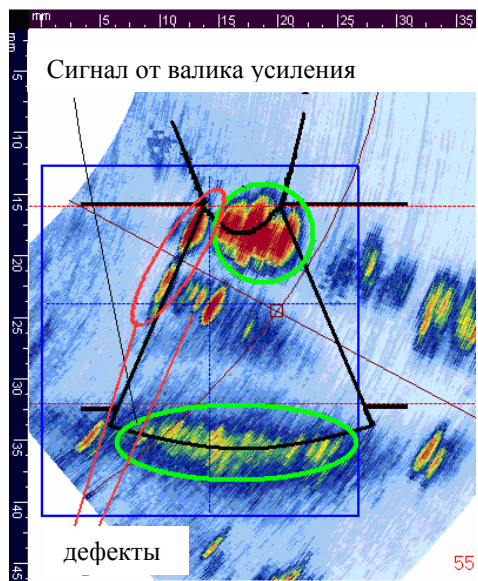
Представление результатов сканирования дефектного участка стальной трубы (образец 3): S-скан с наложенным контуром сварного шва.
